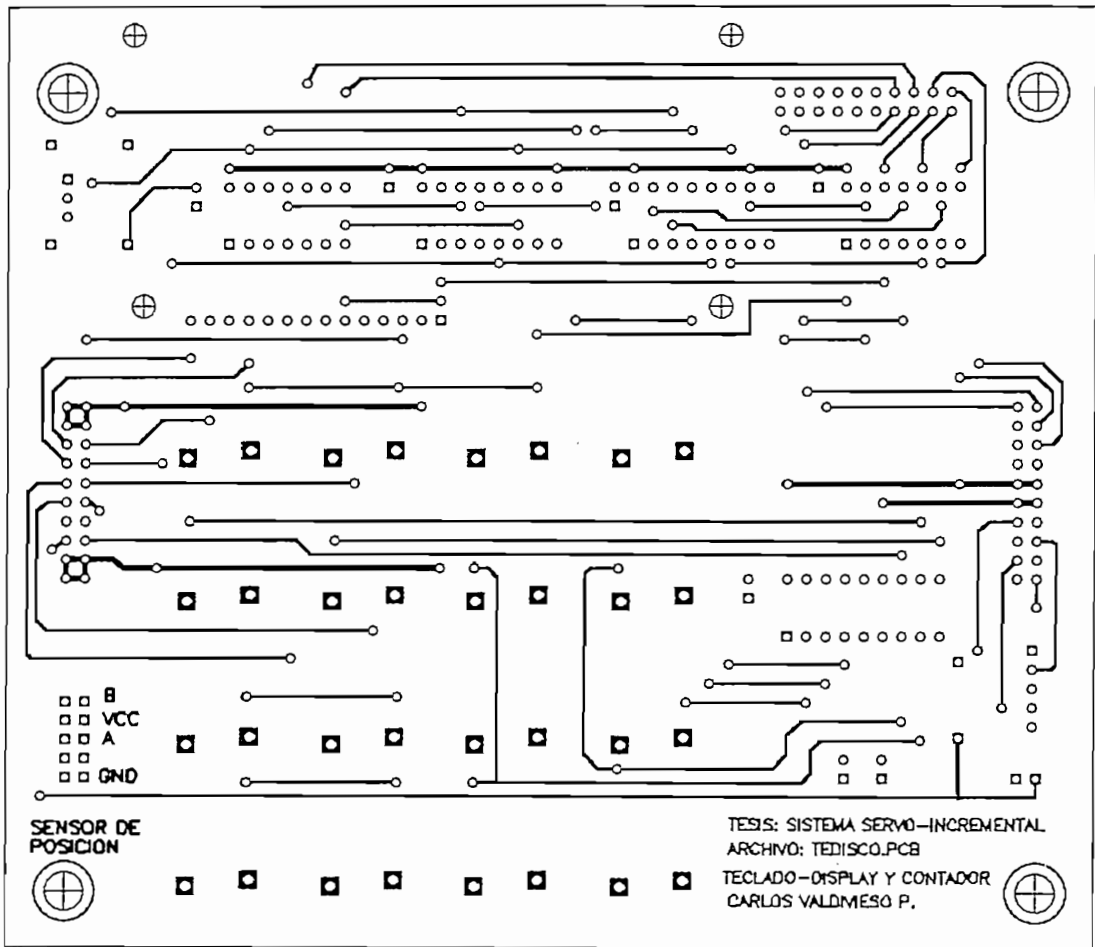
Tarjeta impresa Tedisco , top - soldadura
